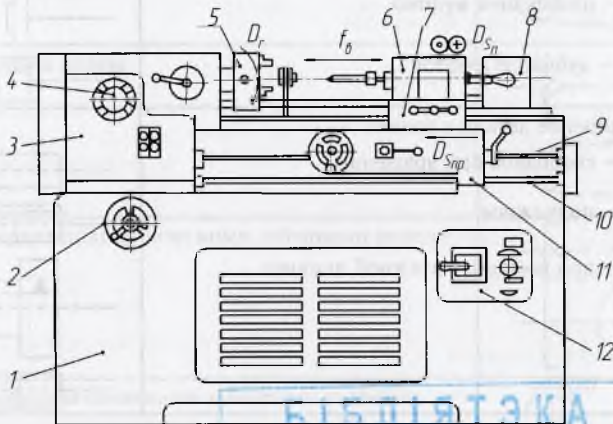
Общий вид модернизированного токарного станка мод. КТС-250
